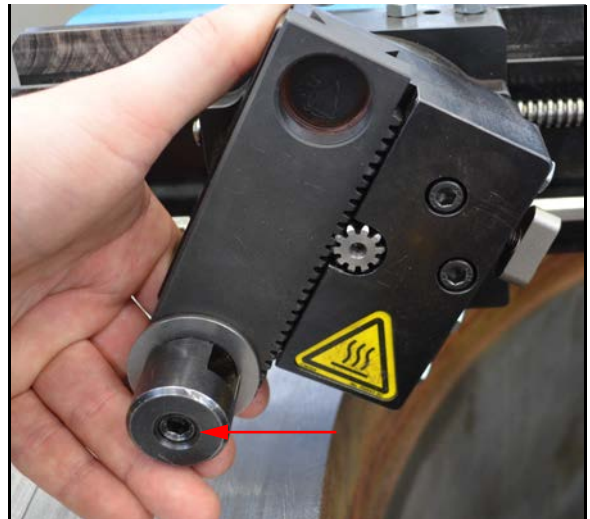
EMPLACEMENT DE LA VIS DE SERRAGE OSCILLANTE
